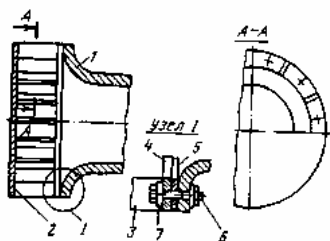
Звукоизолирующий экран для открытой горловины мельницы без насадки:
